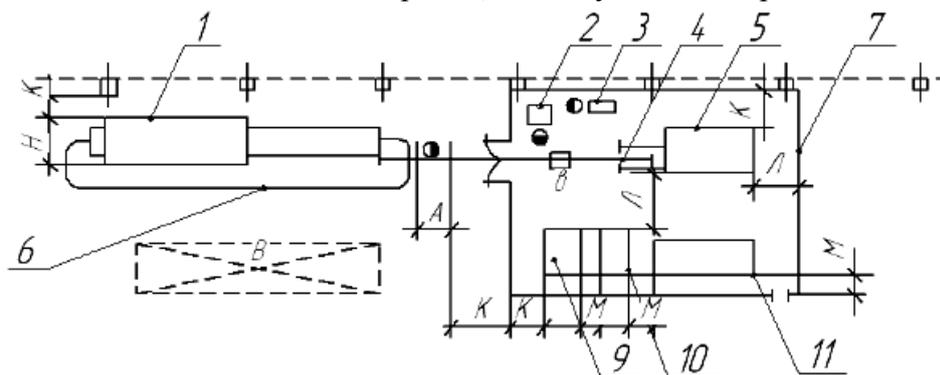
Размещение установки электрошлаковой сварки: 1 – роликовый стэнд механизированный; 2 – направляющие рельсы; 3 – установочная
